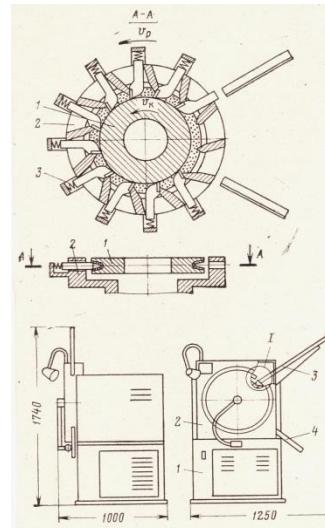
Схема роторного автомата ЗАЗ-2 для обработки задней поверхности резцов
